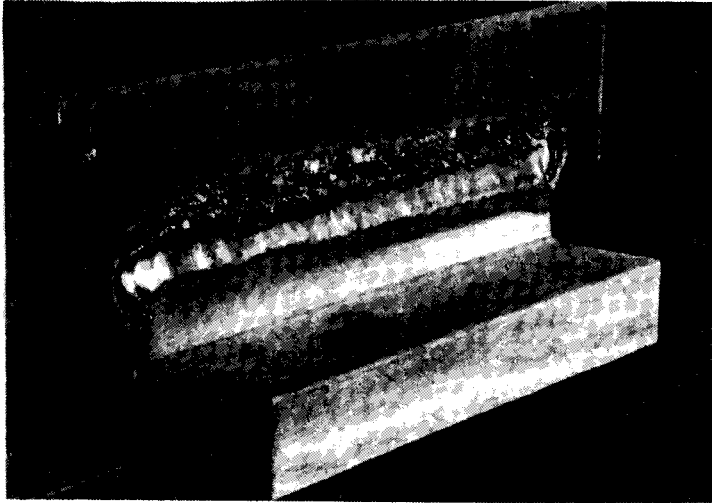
Corrosion feuillette au voisinage d'un cordon de soudure sur l'alliage 7020 T6
